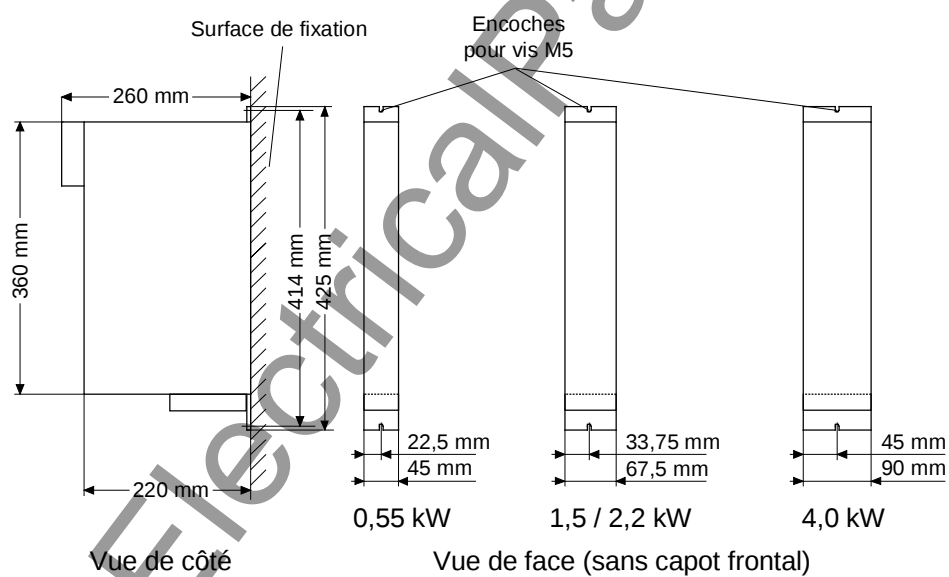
Encombrement, boîtiers de largeur jusqu'à 90 mm
